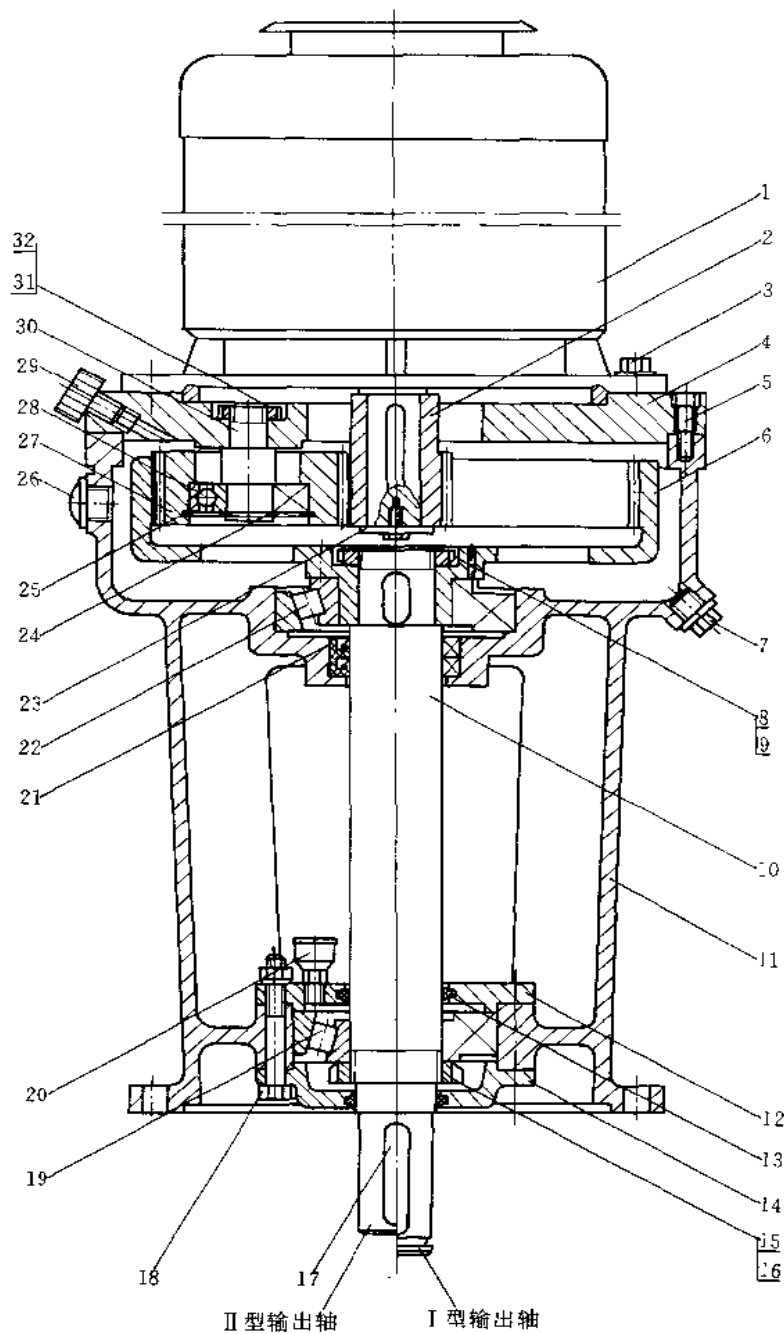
LDC 型立式单级圆柱齿轮减速器
